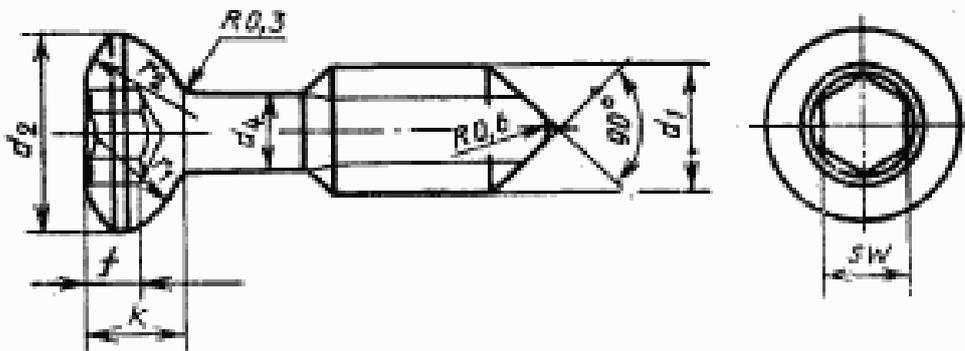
Шуруп с глубокой резьбой (НВ)
